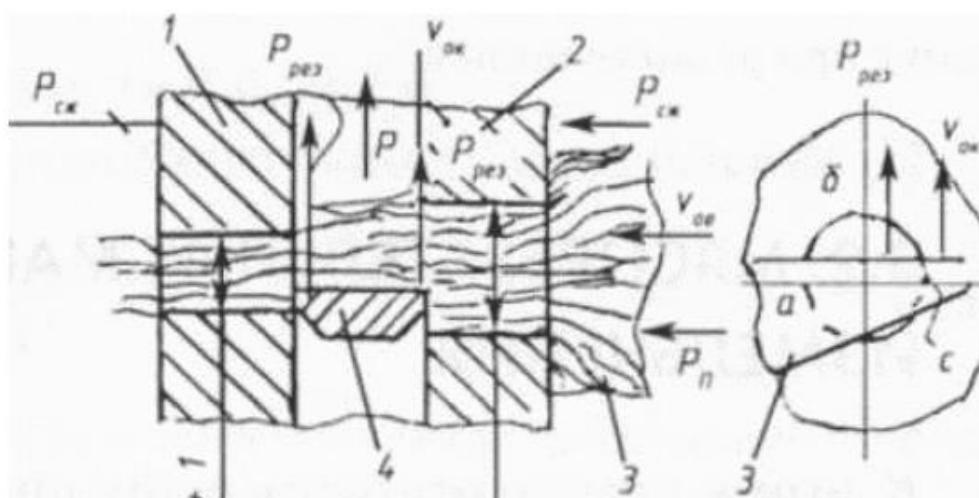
Схема действия режущего механизма нож-решетка:
